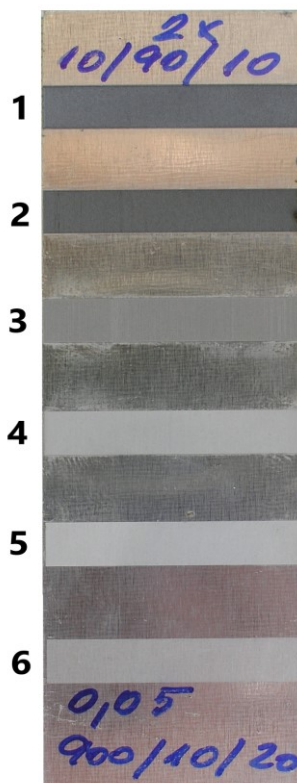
Nákres testovacích vzorků. Převzato z [31]
